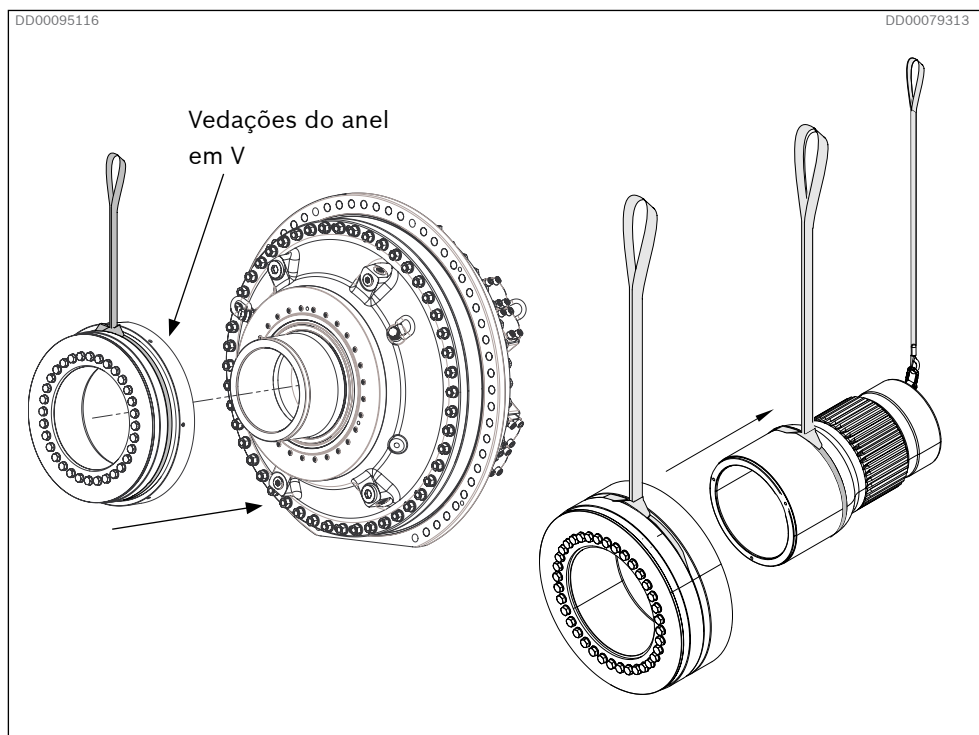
Montagem do disco de contração no adaptador do eixo ou motor de acoplamento
